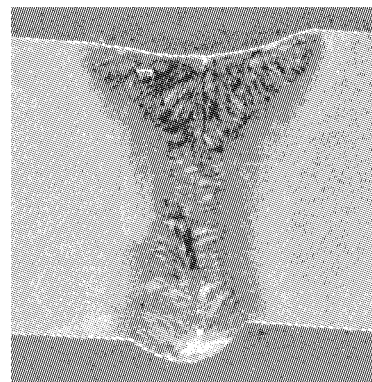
两被焊工件间存在间隙和高度差时的焊缝形状
